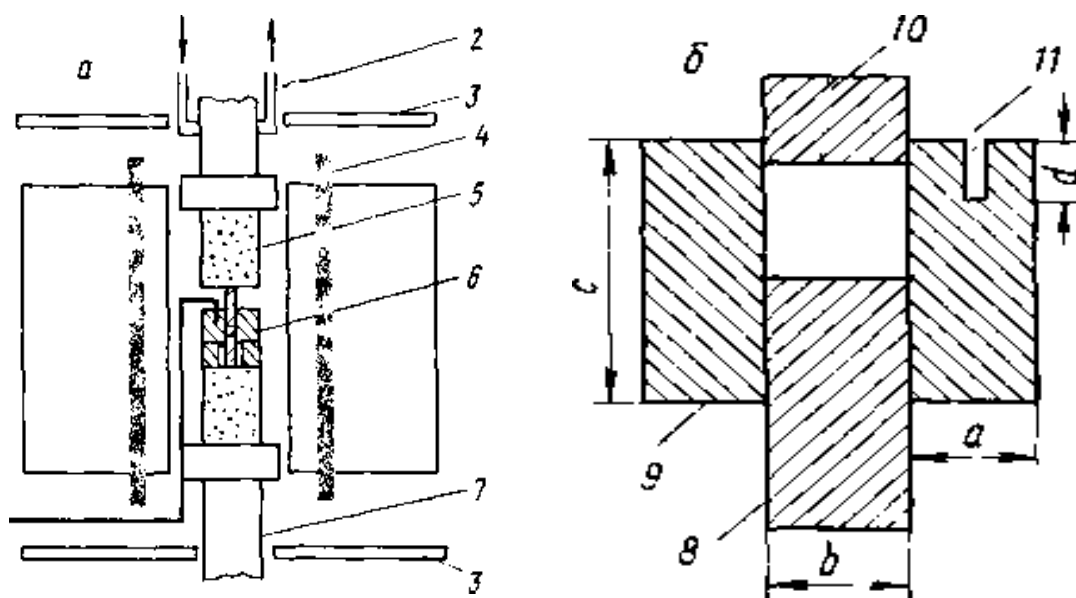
Схема установки (а) и прессформы (б) для горячего прессования: 1 — термопара; 2 — система водного охлаждения; 3 — металлическая теплоотражающая плита; 4 — нагревательный силитовый стержень; 5 — корундовый стержень для передачи давления; 6 — прессформа; 7 — подвижный пуансон; 8 — нижний пуансон; 9 — корпус формы; 10 — верхний пуансон; 11 — щель для термопары
